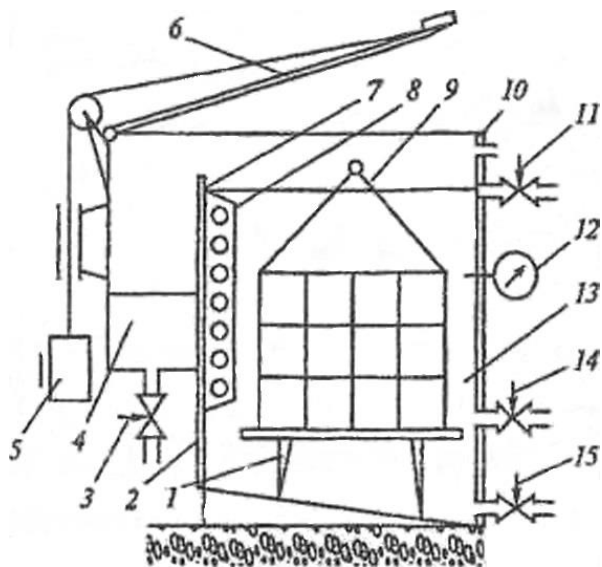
Схема занурювальної установки: 1 – підставка для деталей; 2 – нагрівач; 3 – вентиль зливу оливи; 4 – жолоб флотації; 5 – протизвага; 6 – кришка; 7 – теплоізоляція; 8 – огорожа нагрівача; 9 – контейнер з деталями; 10 – запобіжний злив; 11 – вентиль доливання води; 12 – термометр; 13 – мийний розчин; 14 – вентиль зливу розчину; 15 – вентиль зливу донних відкладень
